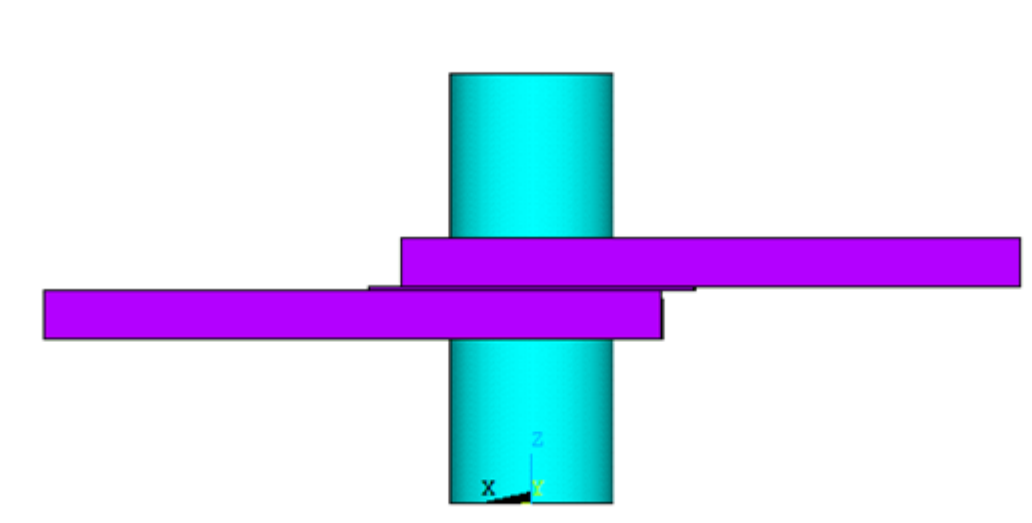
Модель електроконтактного точкового зварювання через багат шаровий прошарок в комплексній системі ANSYS
